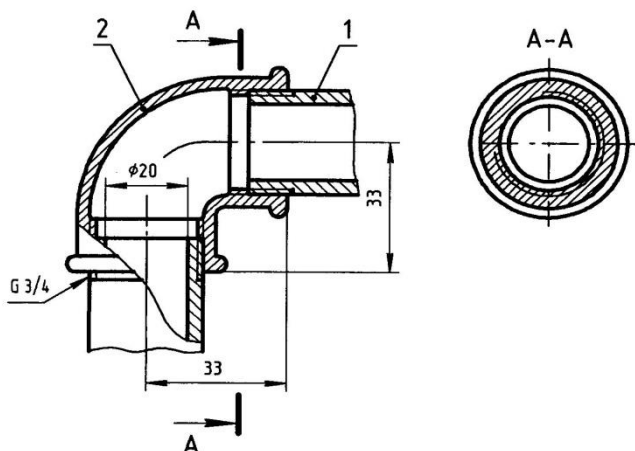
Соединение труб угольником: 1 – труба, 2 – угольник
